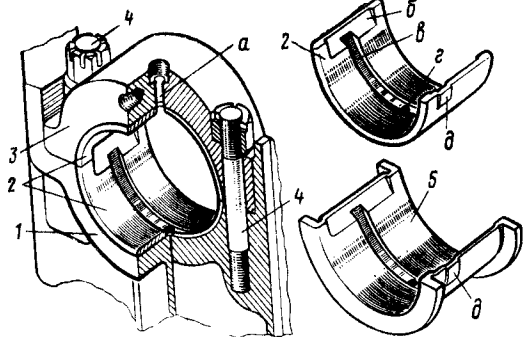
Коренные подшипники коленчатого вала дизеля ПДМ:
